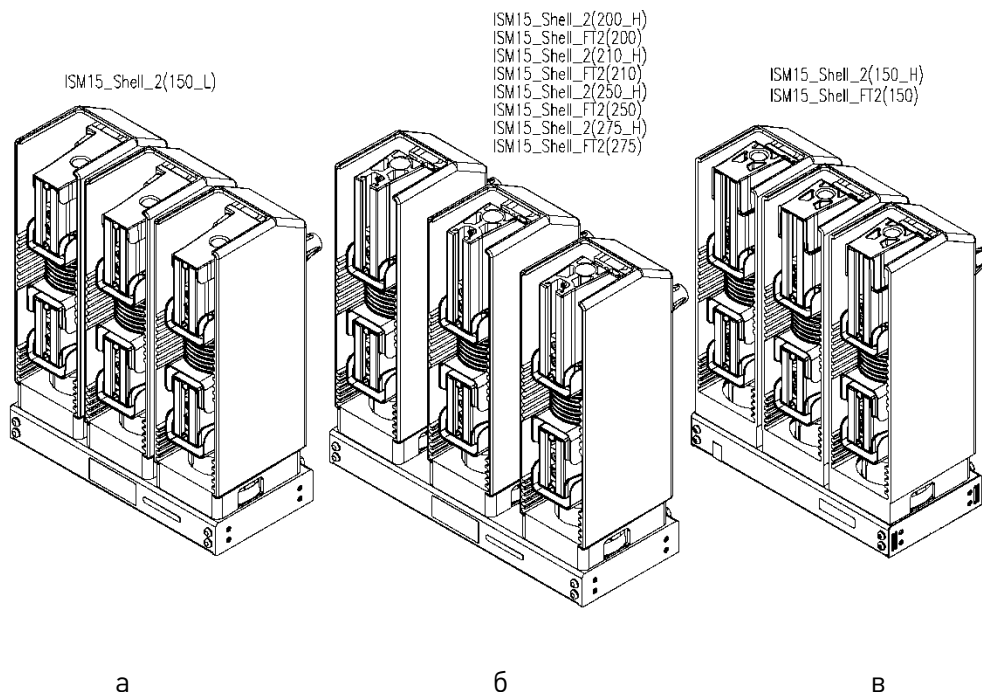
Габаритно-присоединительные размеры КМ
